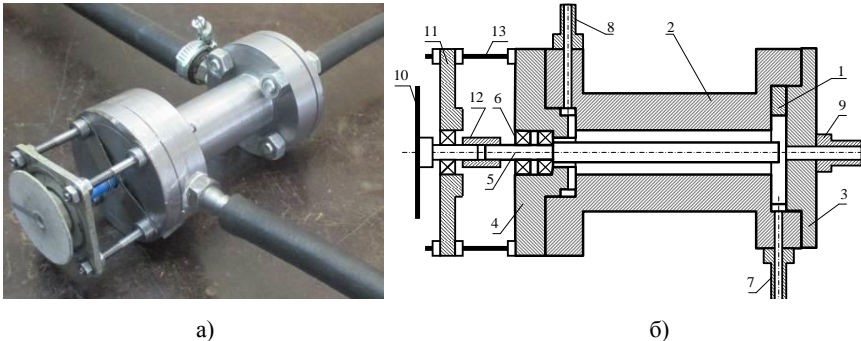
Вихревое устройство: а) общий вид, б) принципиальная схема: 1 – улитка, 2 – корпус вихревой трубы, 3 – прижимная крышка, 4 – крышка со спрямителем потока, 5 – осевой сердечник, 6 – подшипники, 7 – входной штуцер сжатого воздуха, 8 – штуцер «горячего» воздуха, 9 – штуцер «холодного» воздуха, 10 – диск, 11 – обойма, 12 – соединительная втулка, 13 – шпильки
